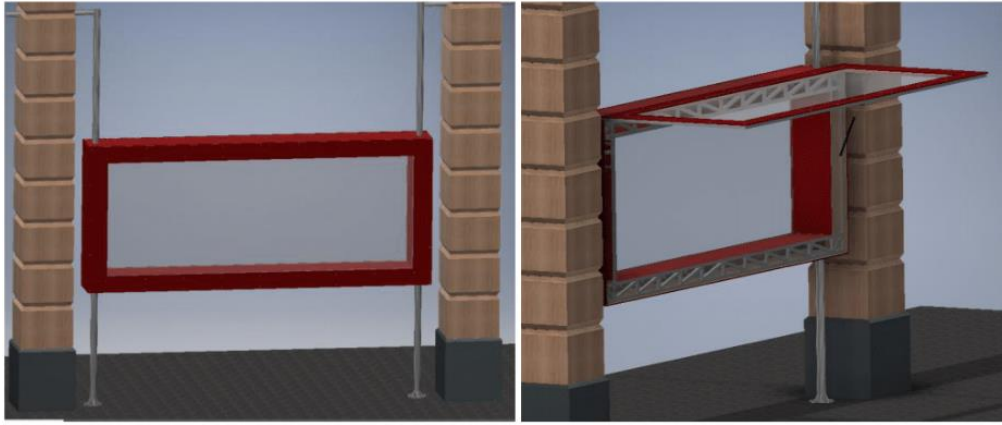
Diseño propuesto de las vitrinas a) Cerrada, b) Abierta. Fuente: Autores
